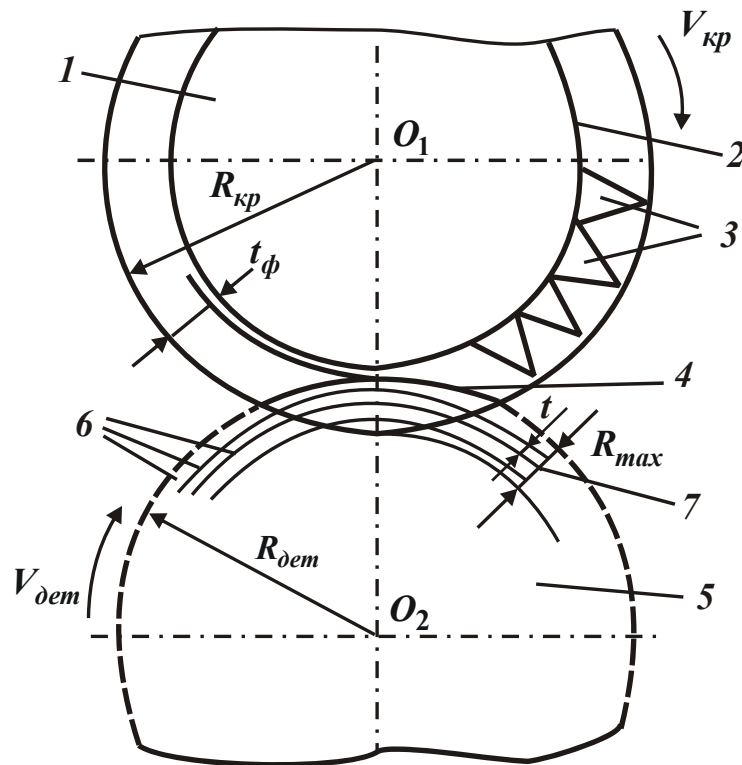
Расчетная схема круглого наружного шлифования: 1 – круг; 2 – уровень связки круга; 3 – режущие зерна; 4 – линия полного съема материала; 5 – деталь; 6 – элементарные цилиндрические оболочки, которыми представлен снимаемый припуск; 7 – слой остаточной шероховатости обработанной поверхности
